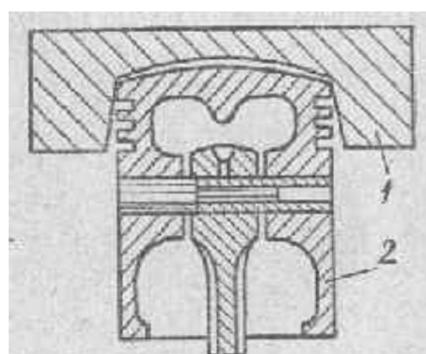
Установка насадки для дополнительного подогрева поршня:
